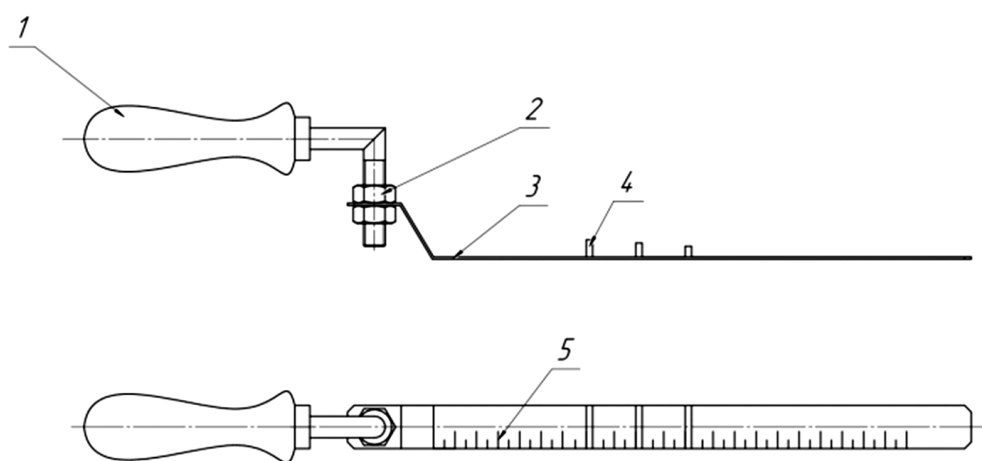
Конструкция усовершенствованного щупа для выявления подкожухового льдообразования:
